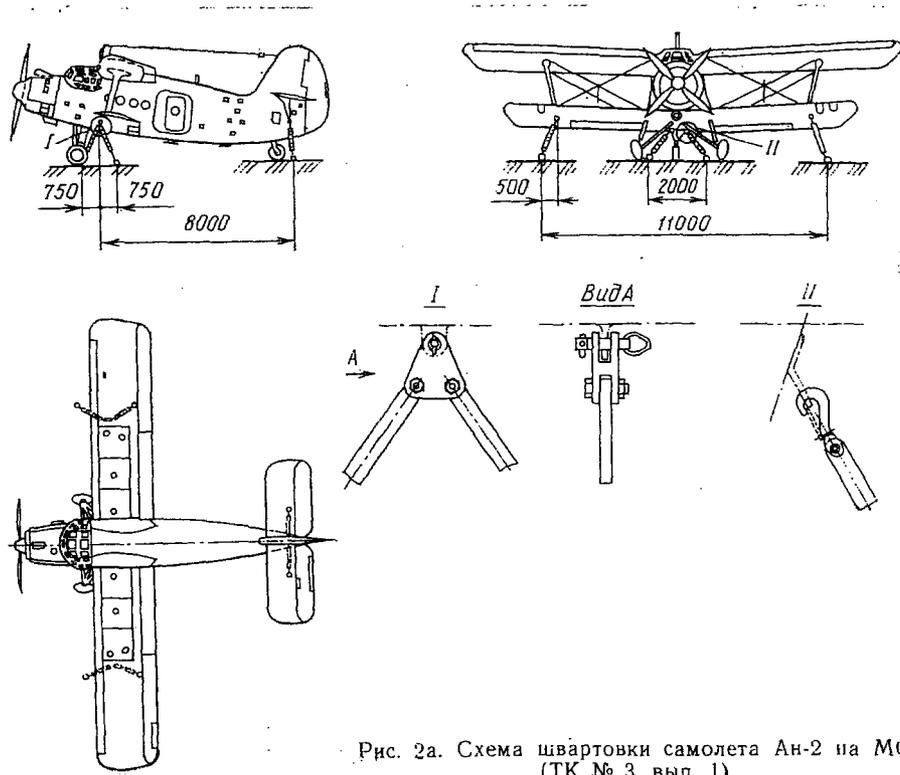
а. Схема швартовки самолета Ан-2 на МС
